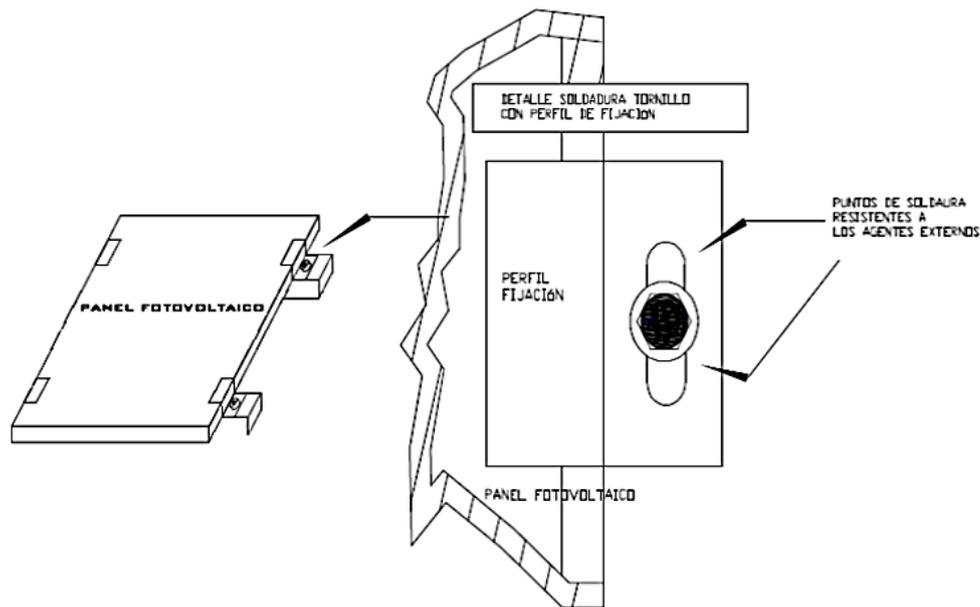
Soldadura empleada para los módulos fotovoltaicos
